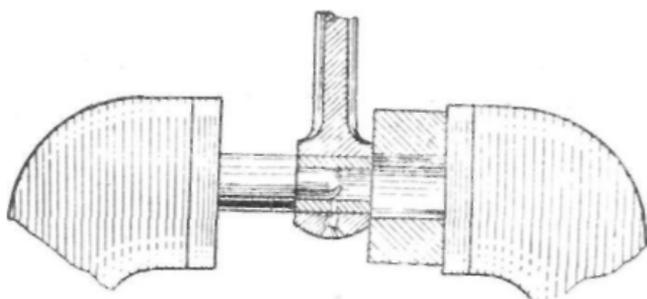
Распрессовка втулки верхней головки шатуна в тисках.
